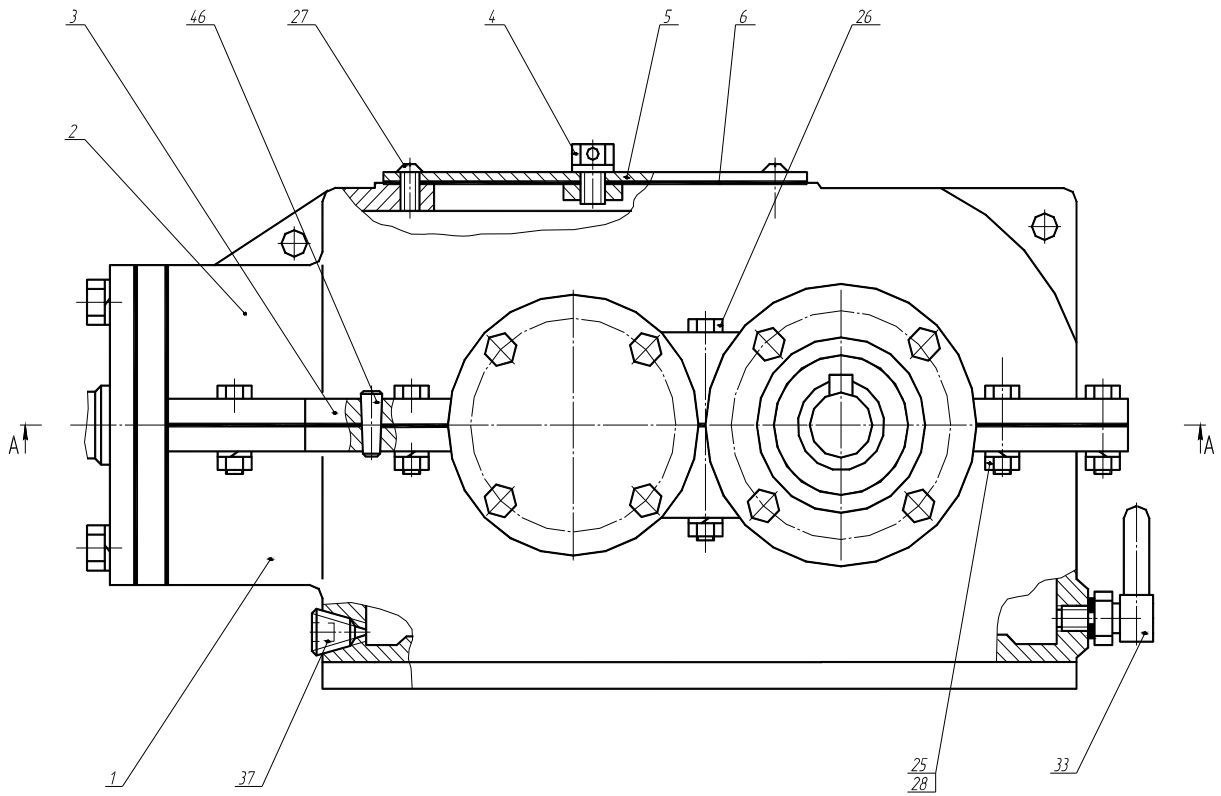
Вариант конструктивного исполнения редуктора коническо-цилиндрического
